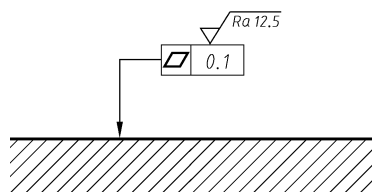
表面结构要求标注在几何公差的框格上
